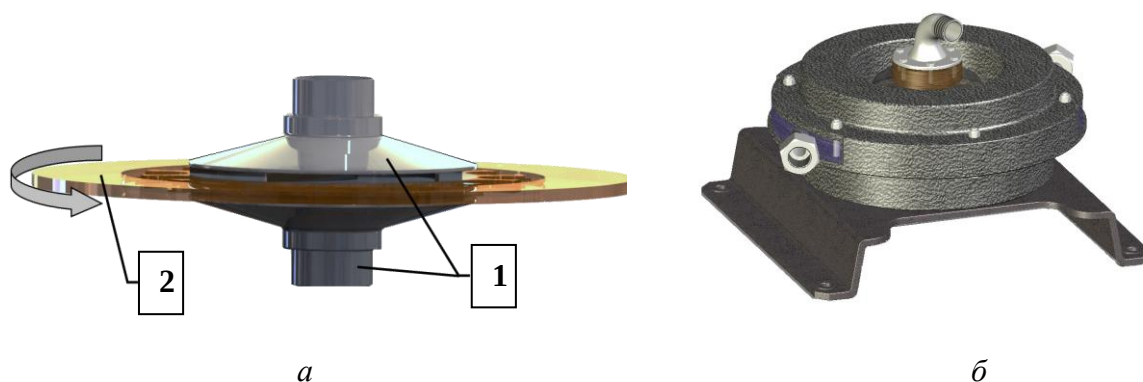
Ротор динамического насоса новой конструкции (а) и его 3D-модель (б): 1 – сдвоенное центробежное колесо; 2 – кольцевой ротор
